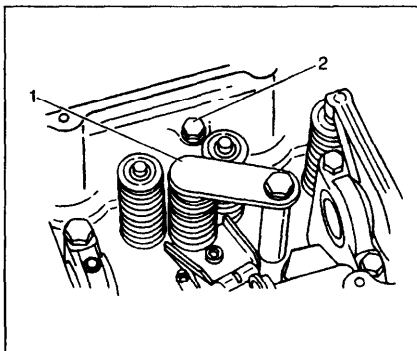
Приспособление для сжатия пружины, установленное на регулируемой форсунке:
